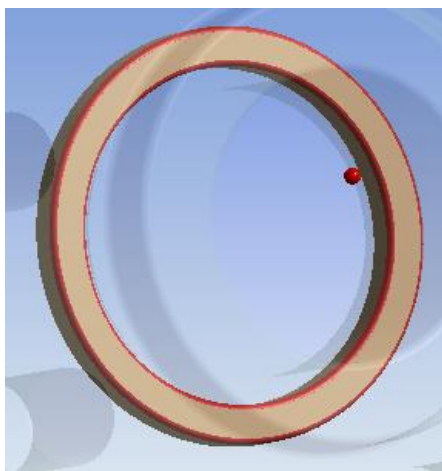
Definição de superfícies do anel em contato com o flange (Autores)
